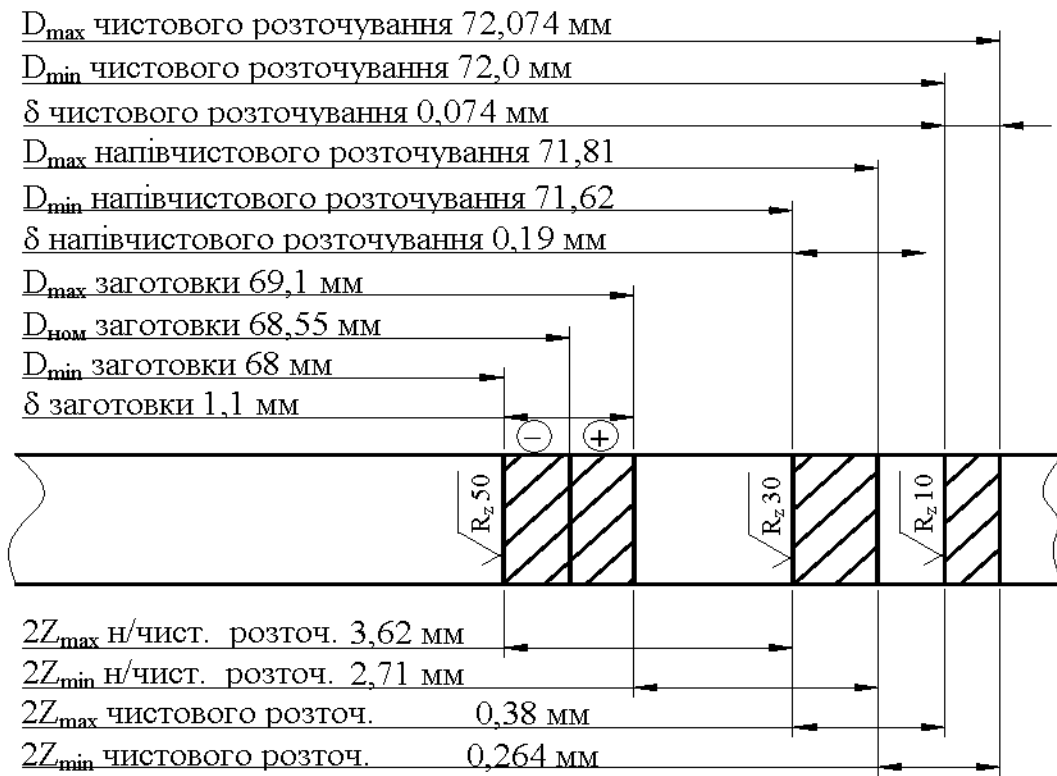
Схема графічного розташування припусків та допусків на обробку поверхні  $\varnothing 72H9^{(+0,074)}$
